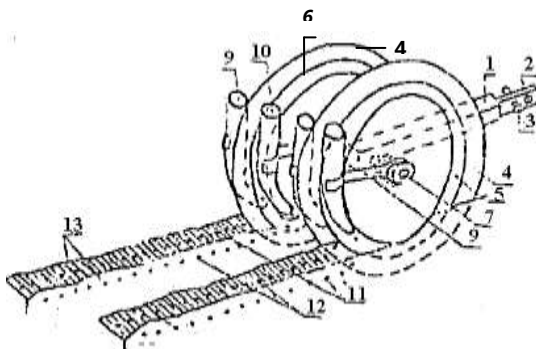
Технологический процесс работы двухдискового четырехстрочного сошника: 1 – корпус; 2 – отверстие; 3 – болт; 4 – диски; 5, 6 – реборды-бороздкообразователи-уплотнители; 7 – ось; 9, 10 – семянаправители; 11 – семена; 12 – удобрения; 13 – бороздка
